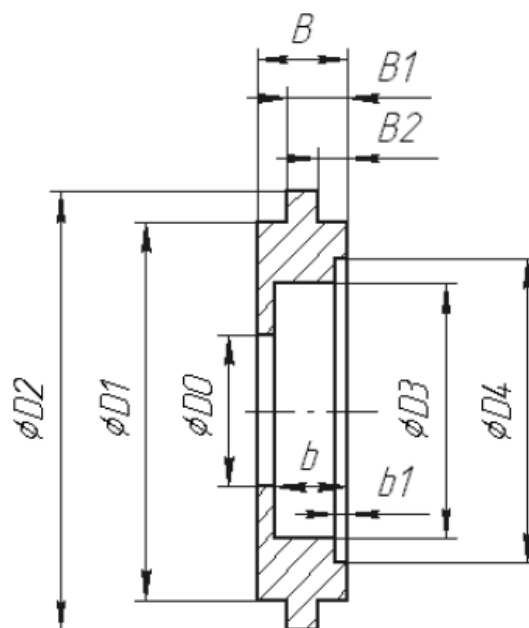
Чертеж сквозной торцевой крышки
